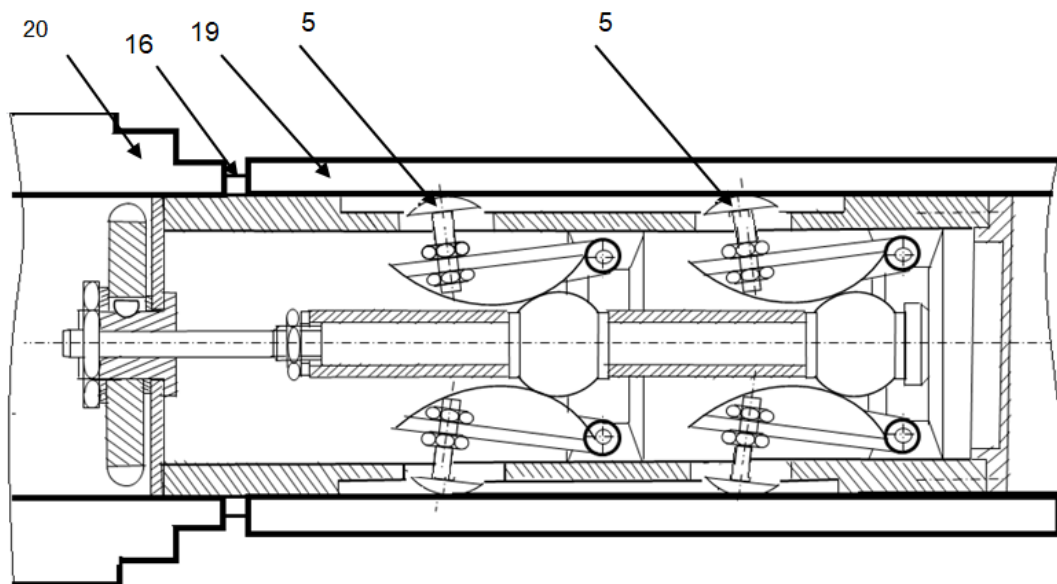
Coupe longitudinale du dispositif conçu en prise sur un tour et en situation d'usinage d'un bout de tube
